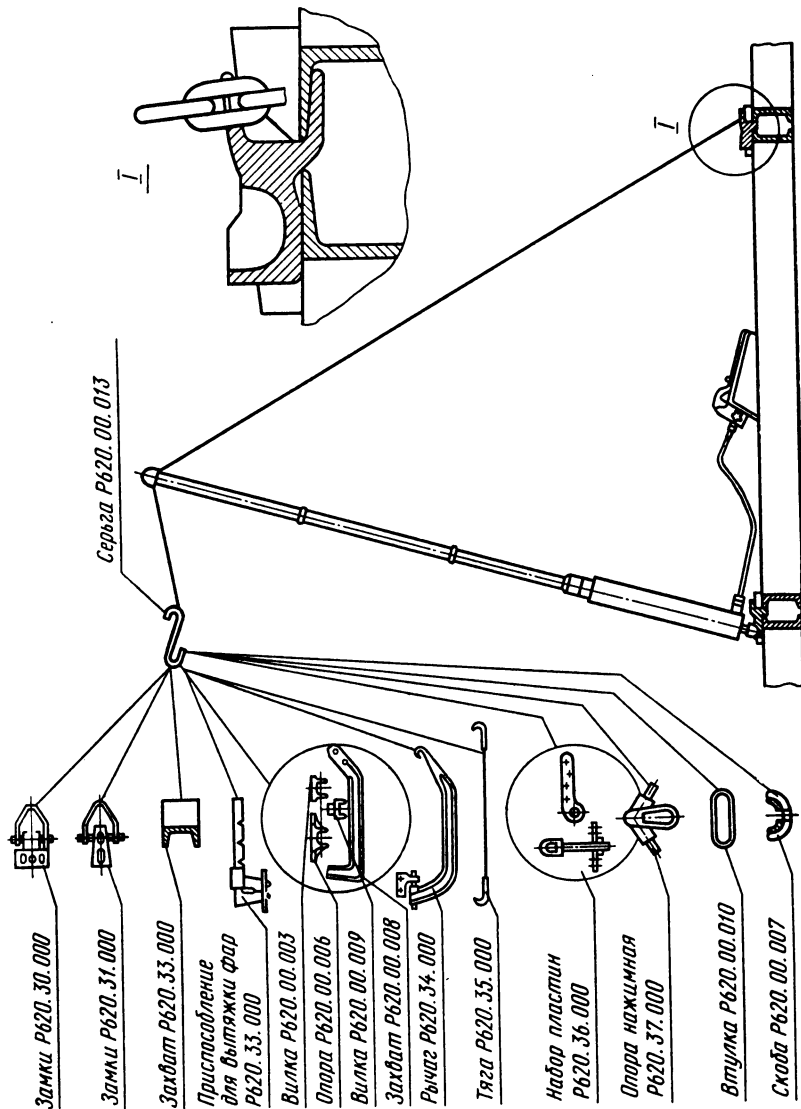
Варианты крепления приспособлений на силовой стойке Р-620
